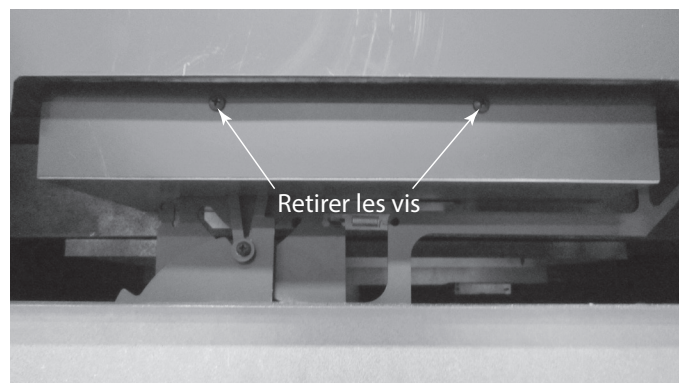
Retrait des vis sur le couvercle de la chambre à air
